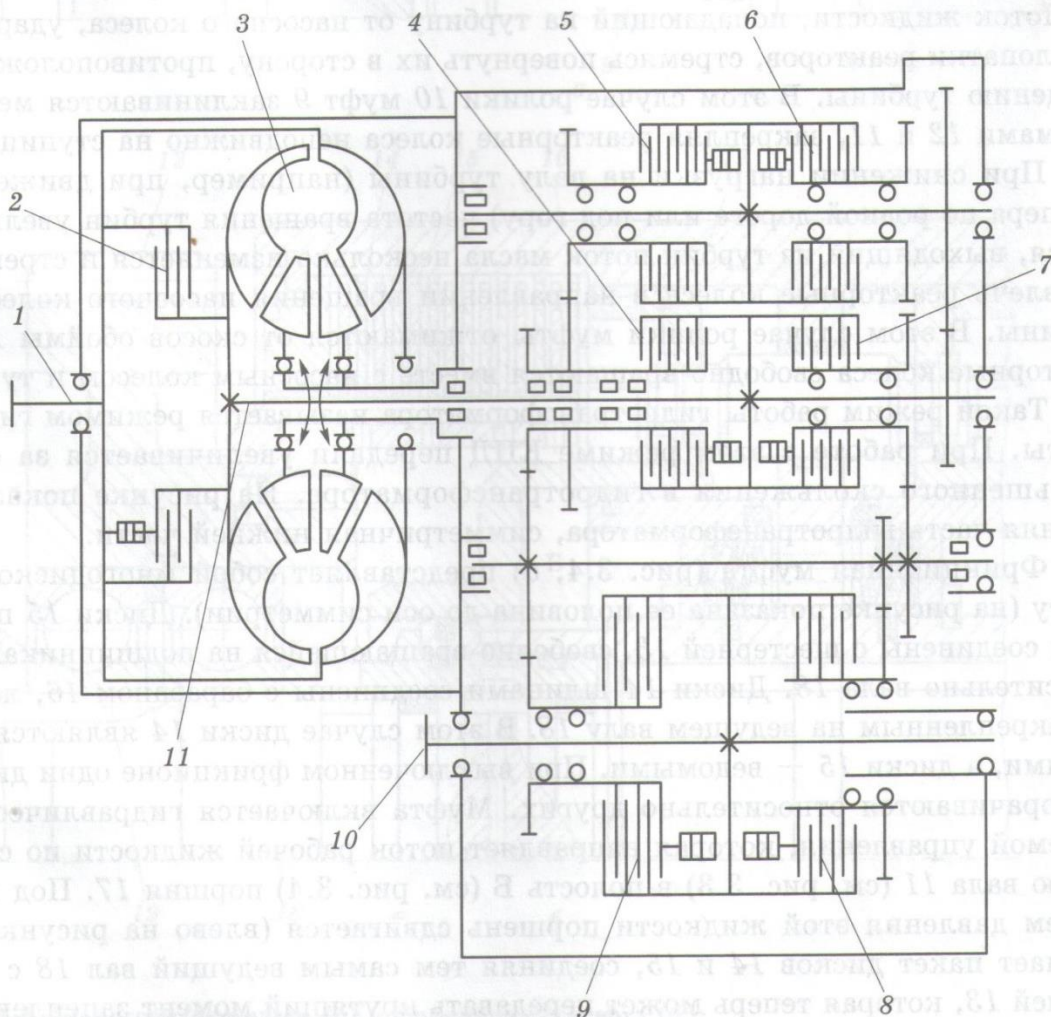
Кинематическая схема гидромеханической коробки передач:
